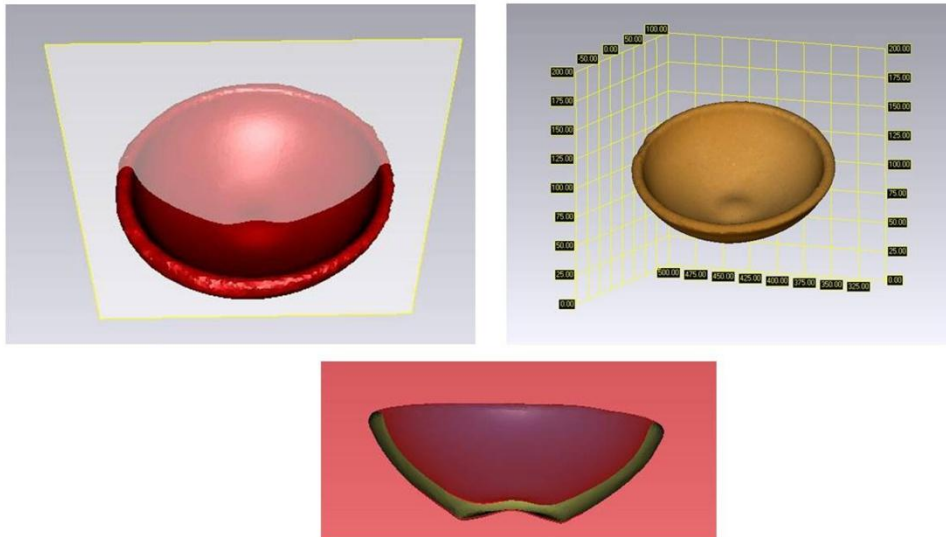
Extracción del perfil a través de la herramienta Sección.
